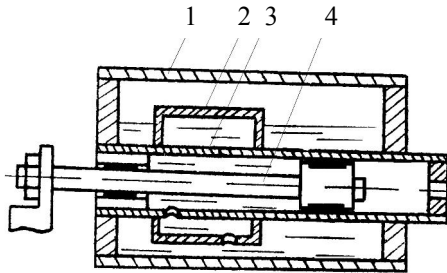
Схема трициліндрового пневматичного накатника:
